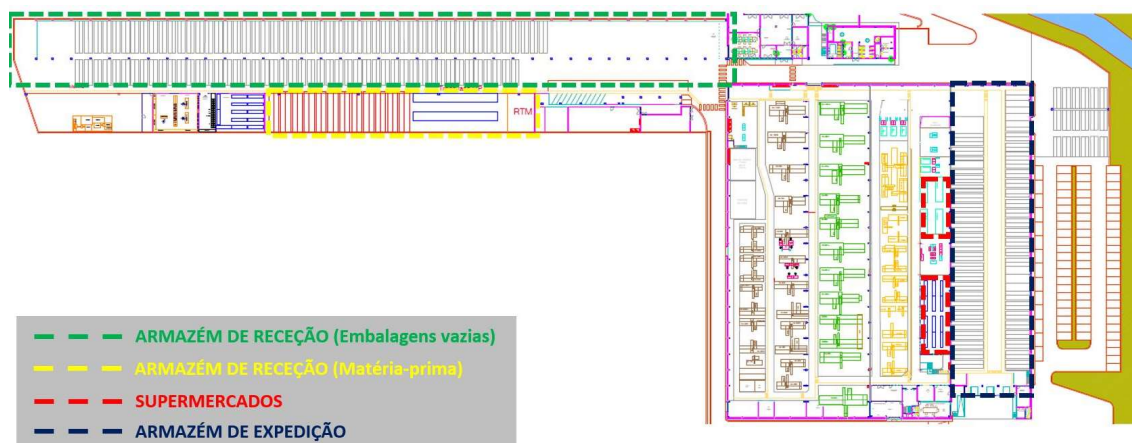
Layout das instalações (Grupo Simoldes, 2022).
